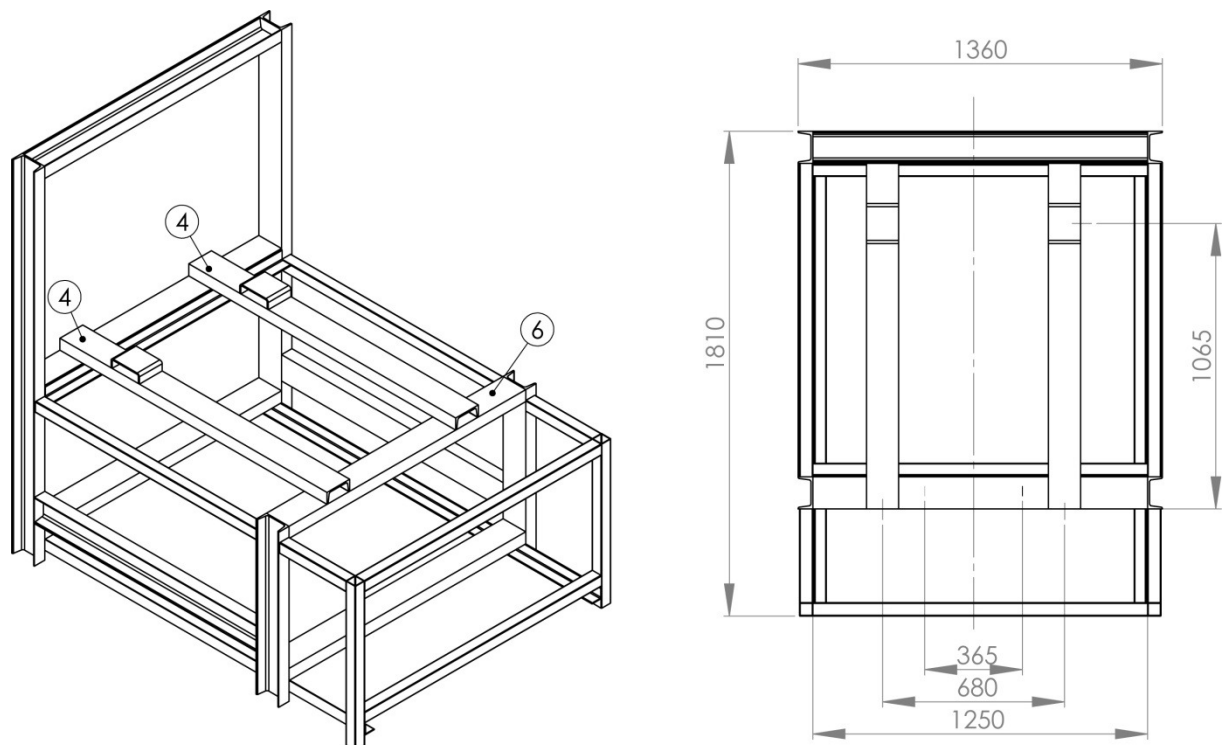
Motorrahmen links isometrisch, rechts Draufsicht
